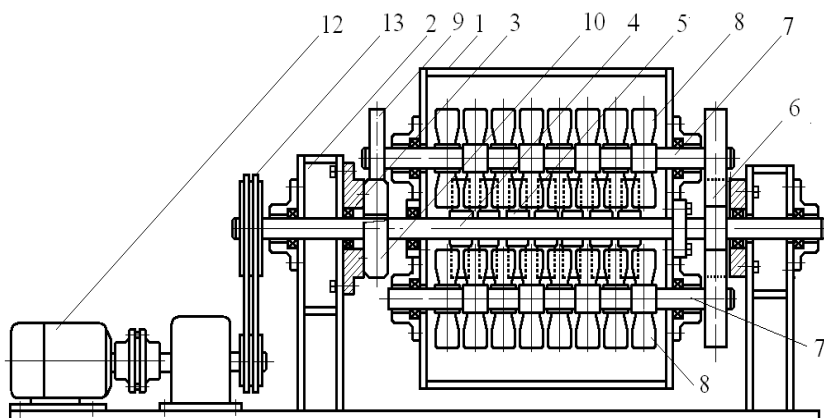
Устройство для получения арболита (общий вид и вид сбоку):
